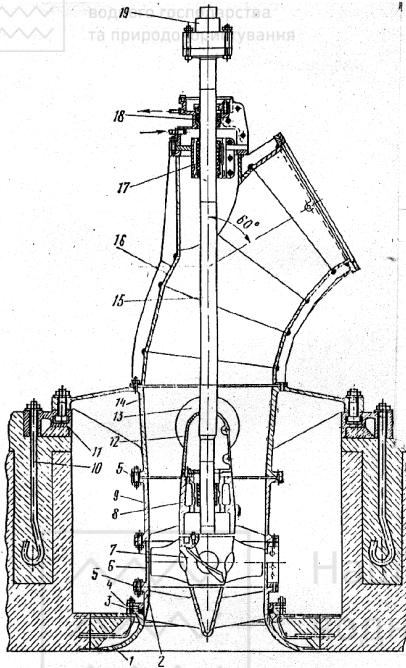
Конструкція осьового насоса: 1- закладне кільце, яке забетоновано в блок насосної станції; 2- перехідний конус; 3- сальникова набивка; 4- нажимне кільце; 5- з'єднання корпусу; 6- камера робочого колеса; 7- втулка робочого колеса з поворотними лопатями; 8- корпус з напрямним підшипником; 9- випрямний апарат; 10- анкерні болти; 11- опори під лапи насоса; 12- кінцева частина обтічного елемента; 13- люк для ревізії насоса; 14- вихідний дифузор; 15- захисний кожух вала; 16- колінчастий відвід; 17- напрямний підшипник; 18- сальникове ущільнення; 19- муфта з'єднання насоса з вертикальним електродвигуном
